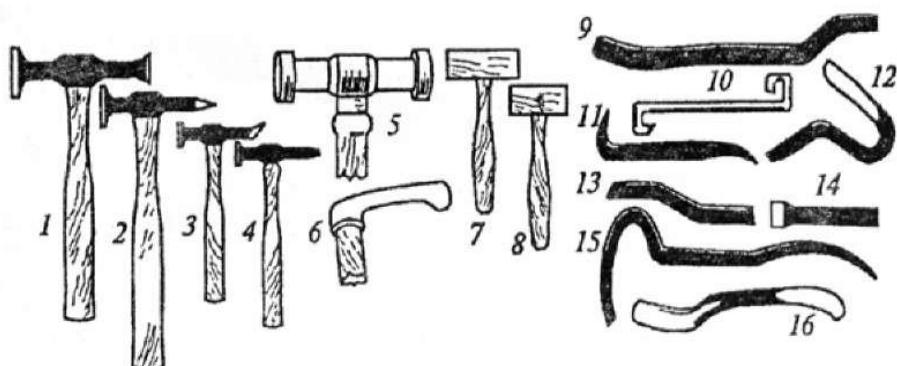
Набор инструментов для удаления вмятин: 1-6 - молотки; 7 и 8 - киянки; 9-19 - оправки
